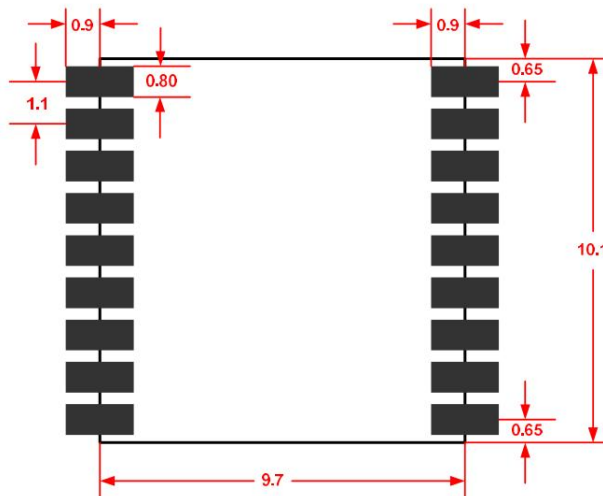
正视图, M210H PCB 封装 (单位: 毫米)
